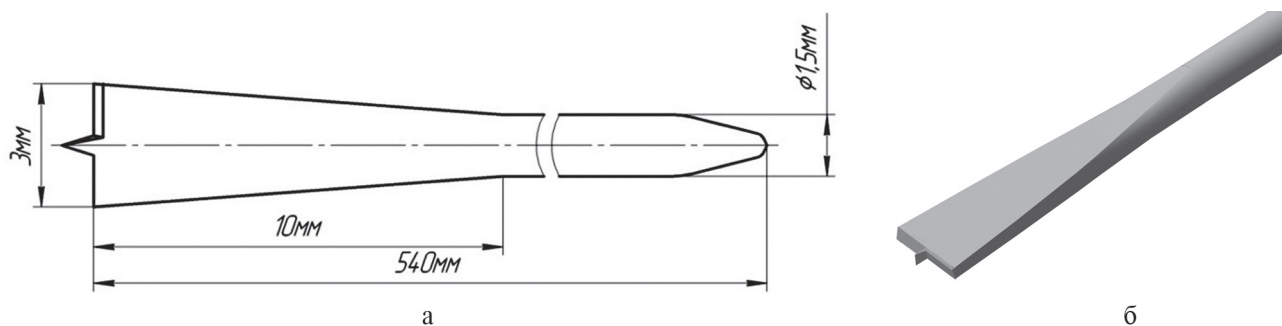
Тонкое буровое сверло: а – основные размеры сверла; б – модель режущей головки тонкого бурового сверла
